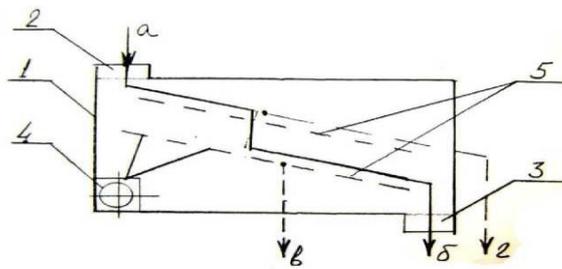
Технологическая схема сепаратора: 1 - корпус; 2 - приёмное устройство; 3 - выпускные устройства; 4 - привод; 5 - рабочий орган(сита); а - исходная смесь; б - очищенное зерно; в - мелкие примеси; г - крупные примеси.
